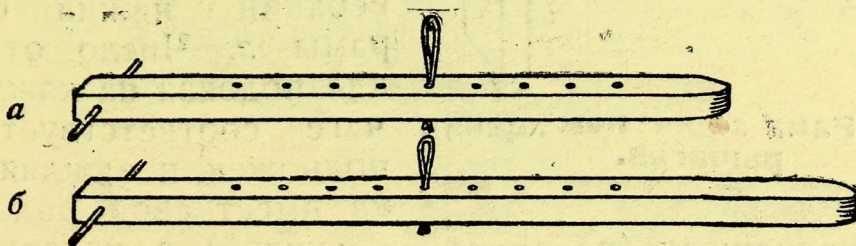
Рычаги: верхний *a* и нижний *б*.
